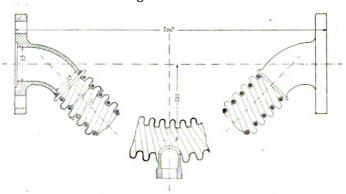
Geschweißter Schlauch als Heizschlauch zwischen Lokomotive und Tender.
